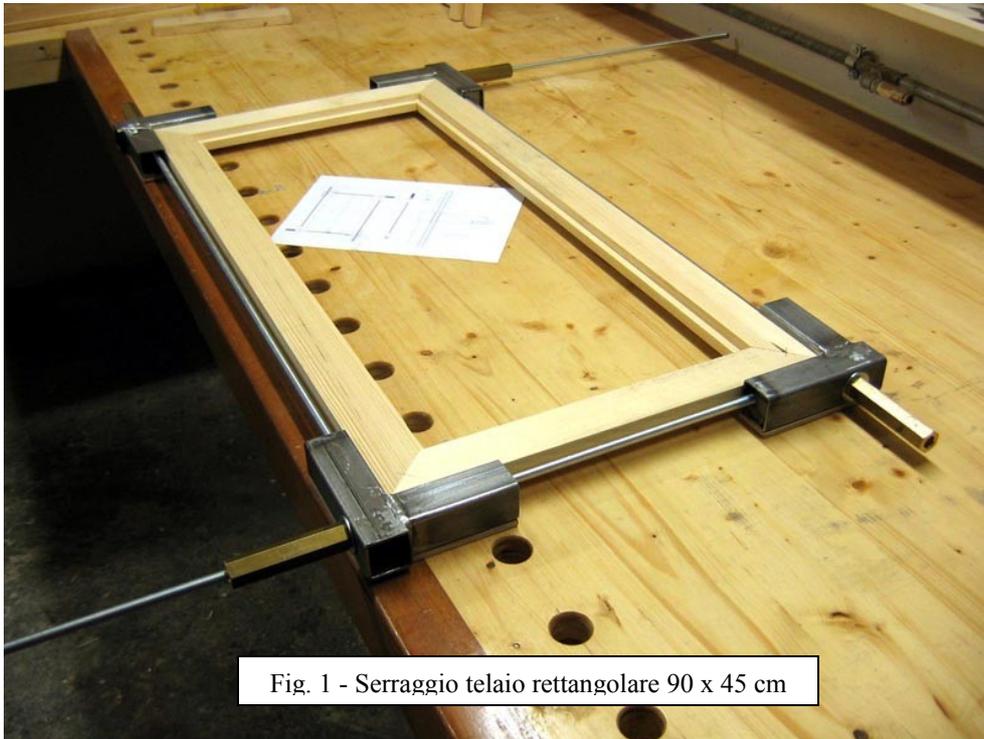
Serraggio telaio rettangolare 90 x 45 cm
